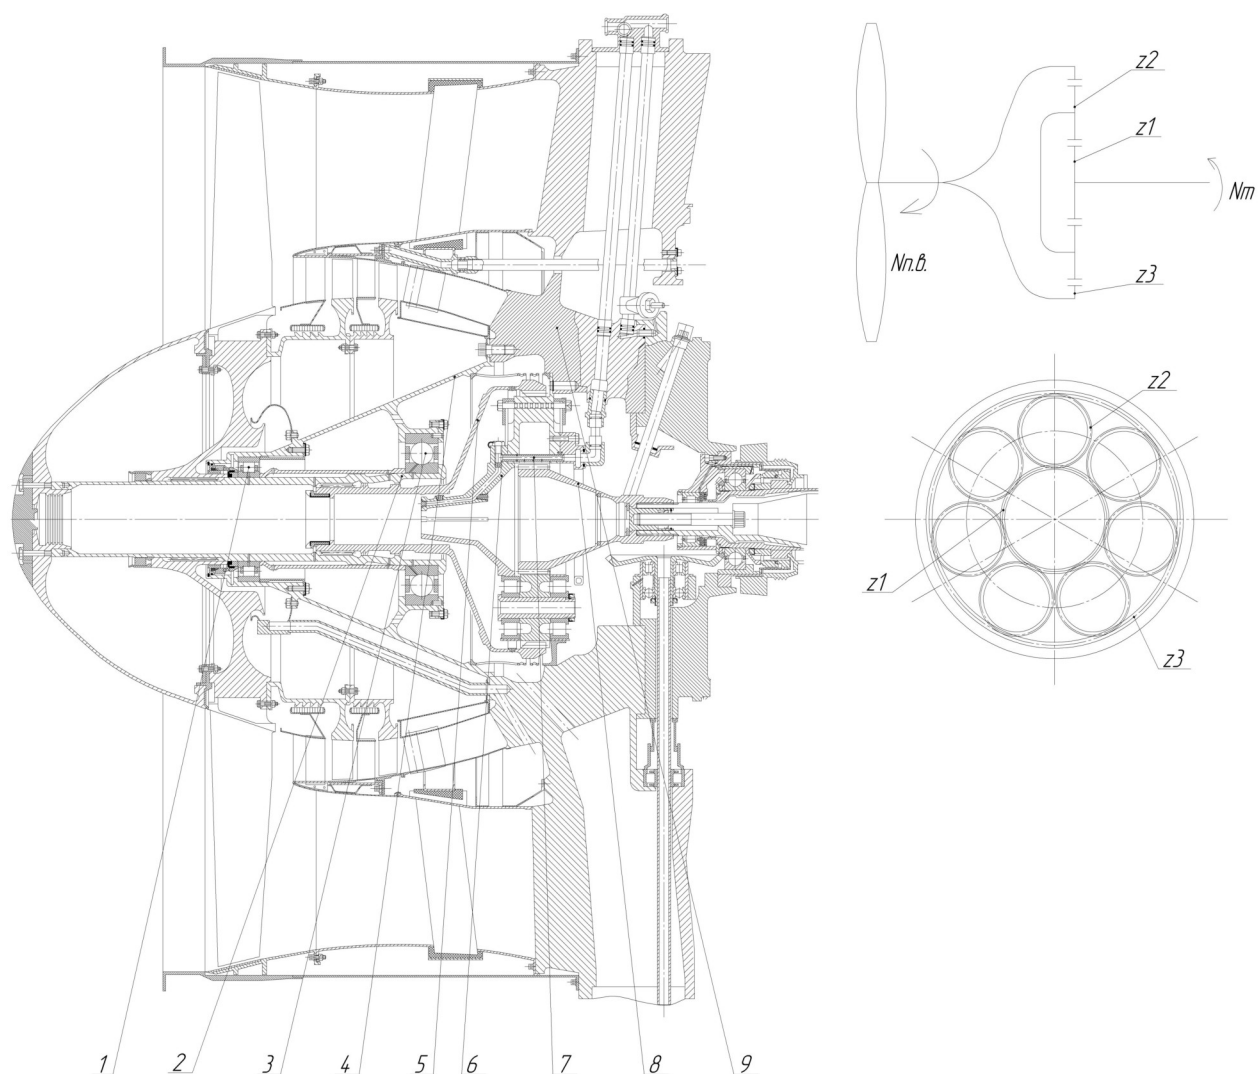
Простой редуктор ТРДД LF 507 (полученный из планетарного, остановкой водила):
